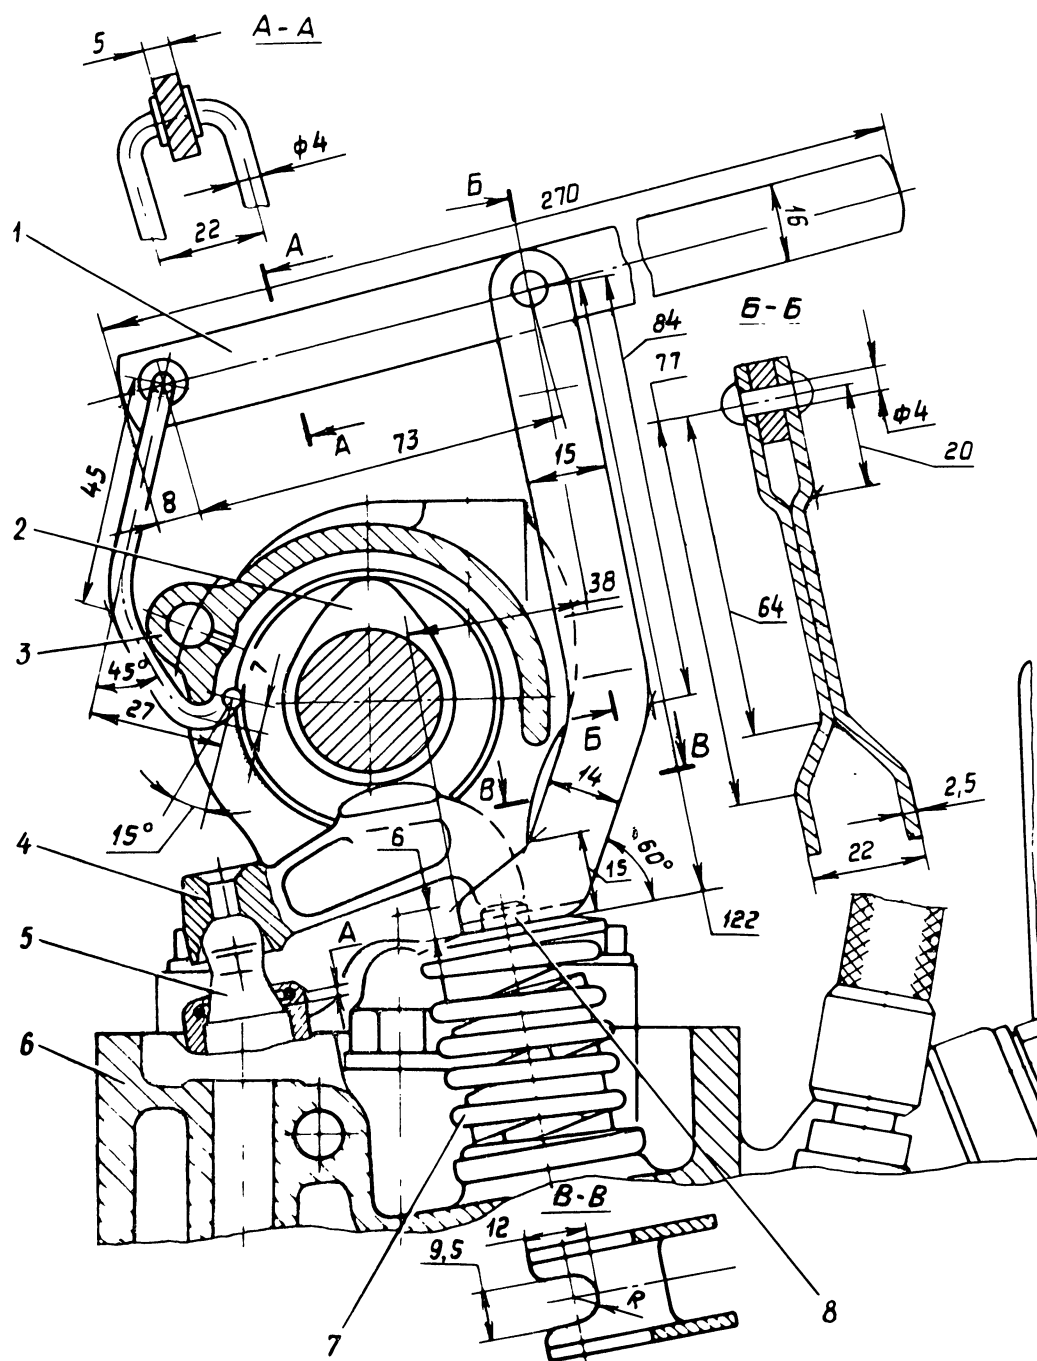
Приспособление для отжима пружин клапанов двигателя:
